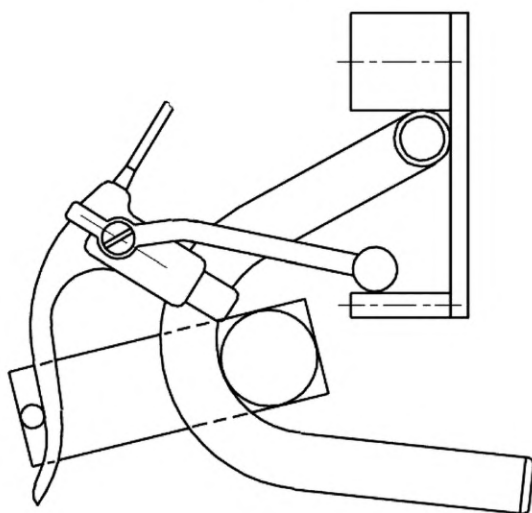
Метод размещения размерного шаблона на тормозных ручках и рулях для типа С
